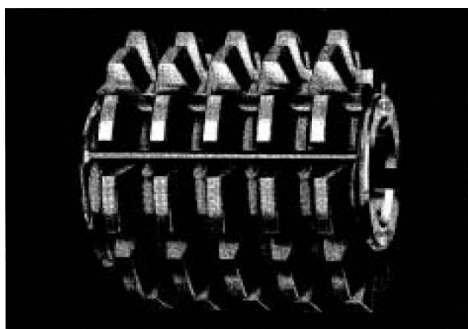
Ferramenta de corte para talhagem de engrenagens [3]
